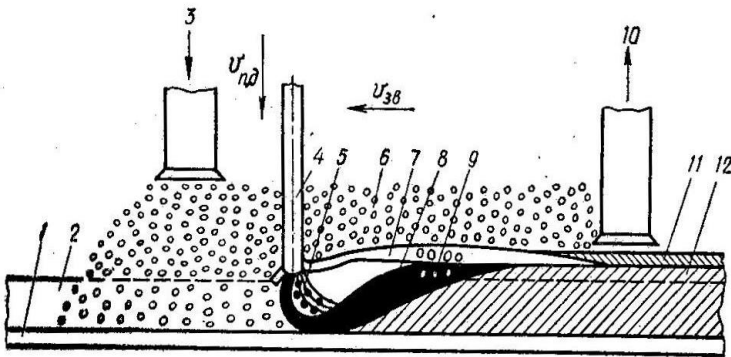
Схема процесу автоматичного зварювання під флюсом
